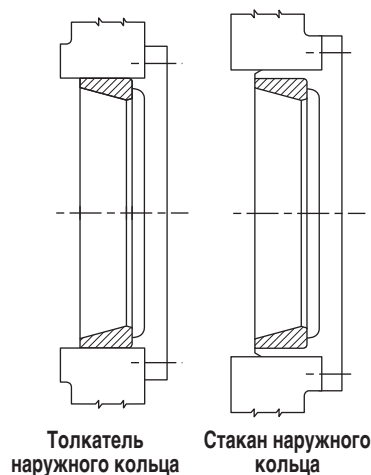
Приспособления для регулировки подшипников (схема монтажа «О»).
